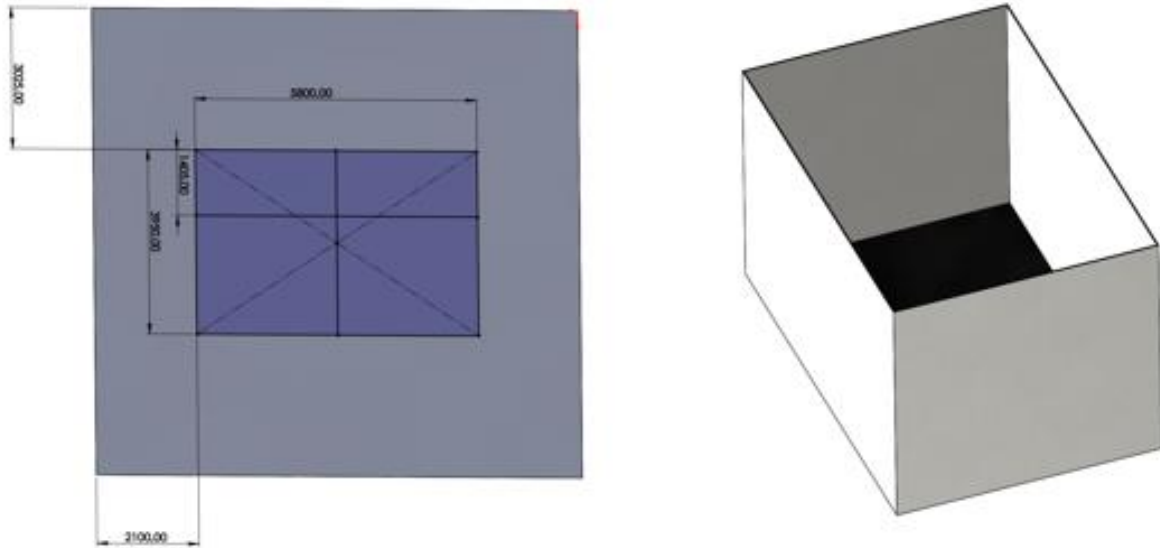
8 Representación de la estructura de la celda de soldadura
